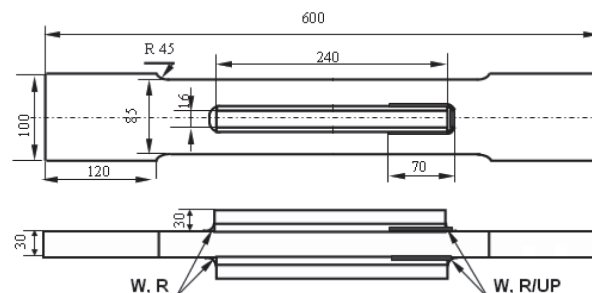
種々の状態で疲労試験を行った溶接継手試験片形状（W-As Weld, R-ガウジング後の補修溶接, R/UP-ガウジングと補修溶接後のUP処理）
